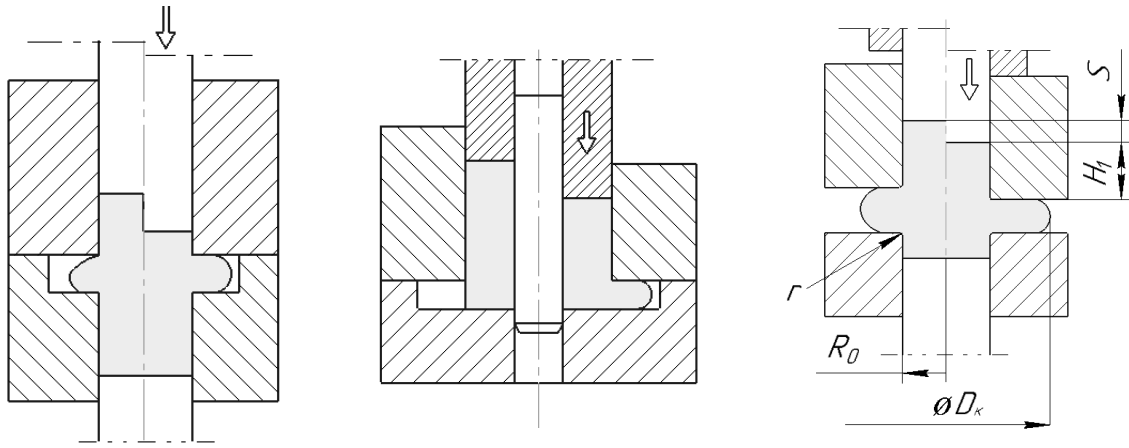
Схема радіального видавлювання деталей з фланцем
